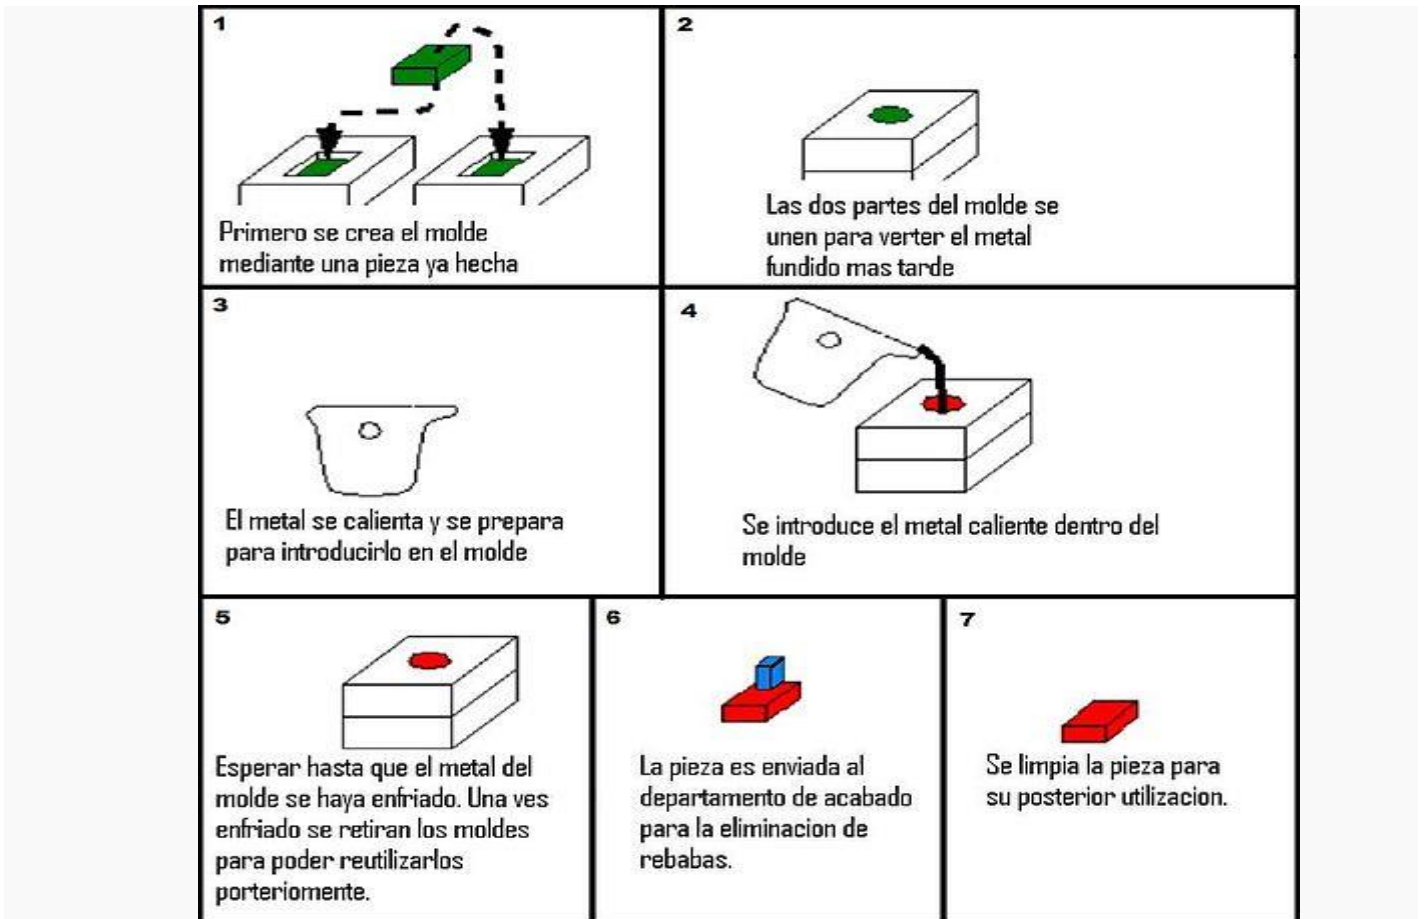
Moldeo en arena verde: Proceso para la fabricación de piezas mediante el proceso de moldeo en verde.
